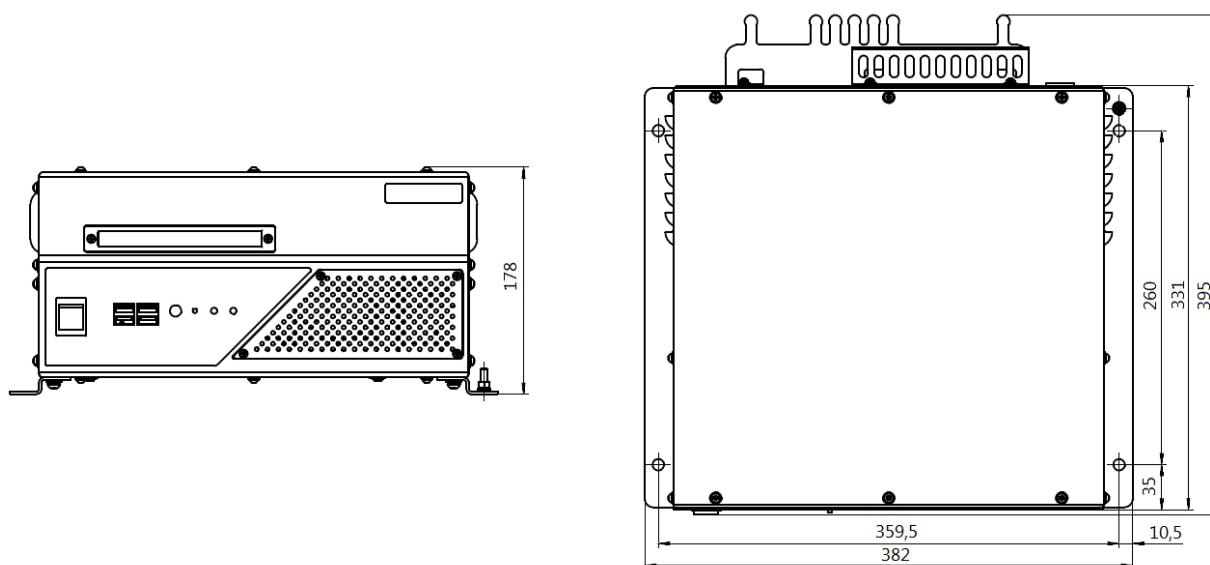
Габаритные размеры изделия типа СБК-127
